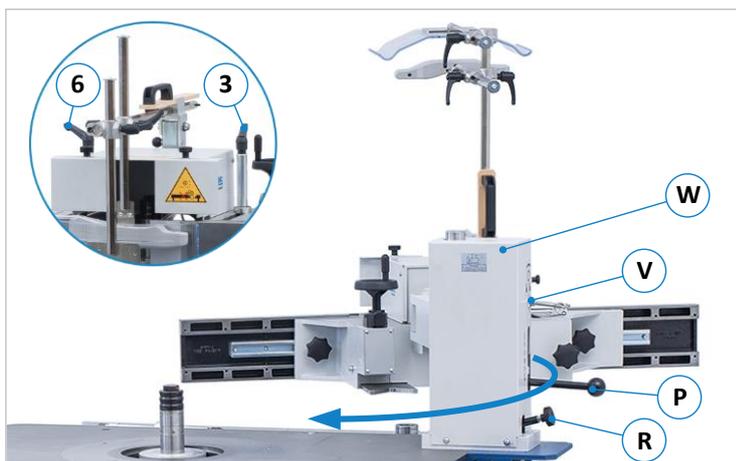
Hydraulische Wegschwenkvorrichtung
